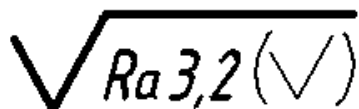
Обозначение шероховатости одинаковой для части поверхностей
